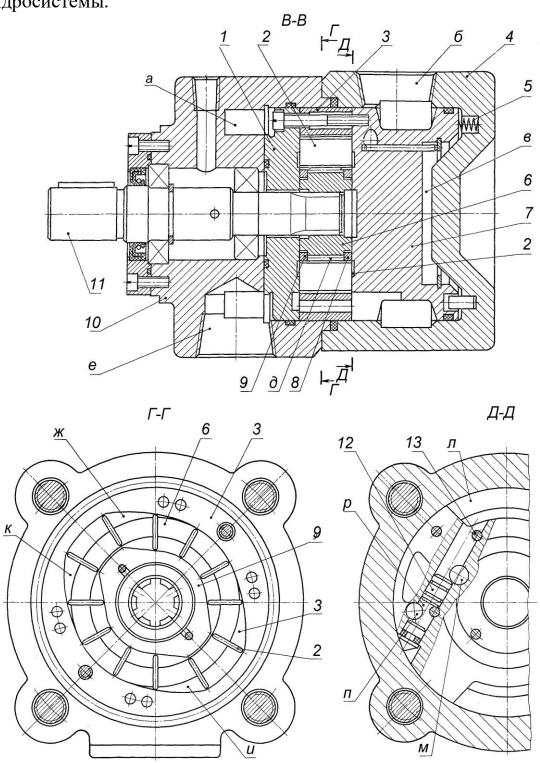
Пластинчатый гидромотор двойного действия типа Г16
